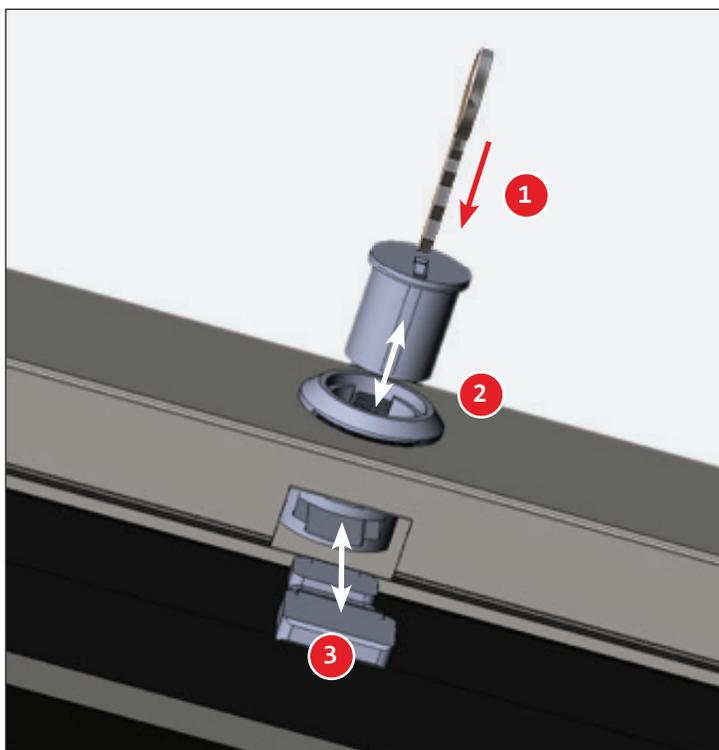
Vista inferior del desmontaje/montaje de los componentes.
